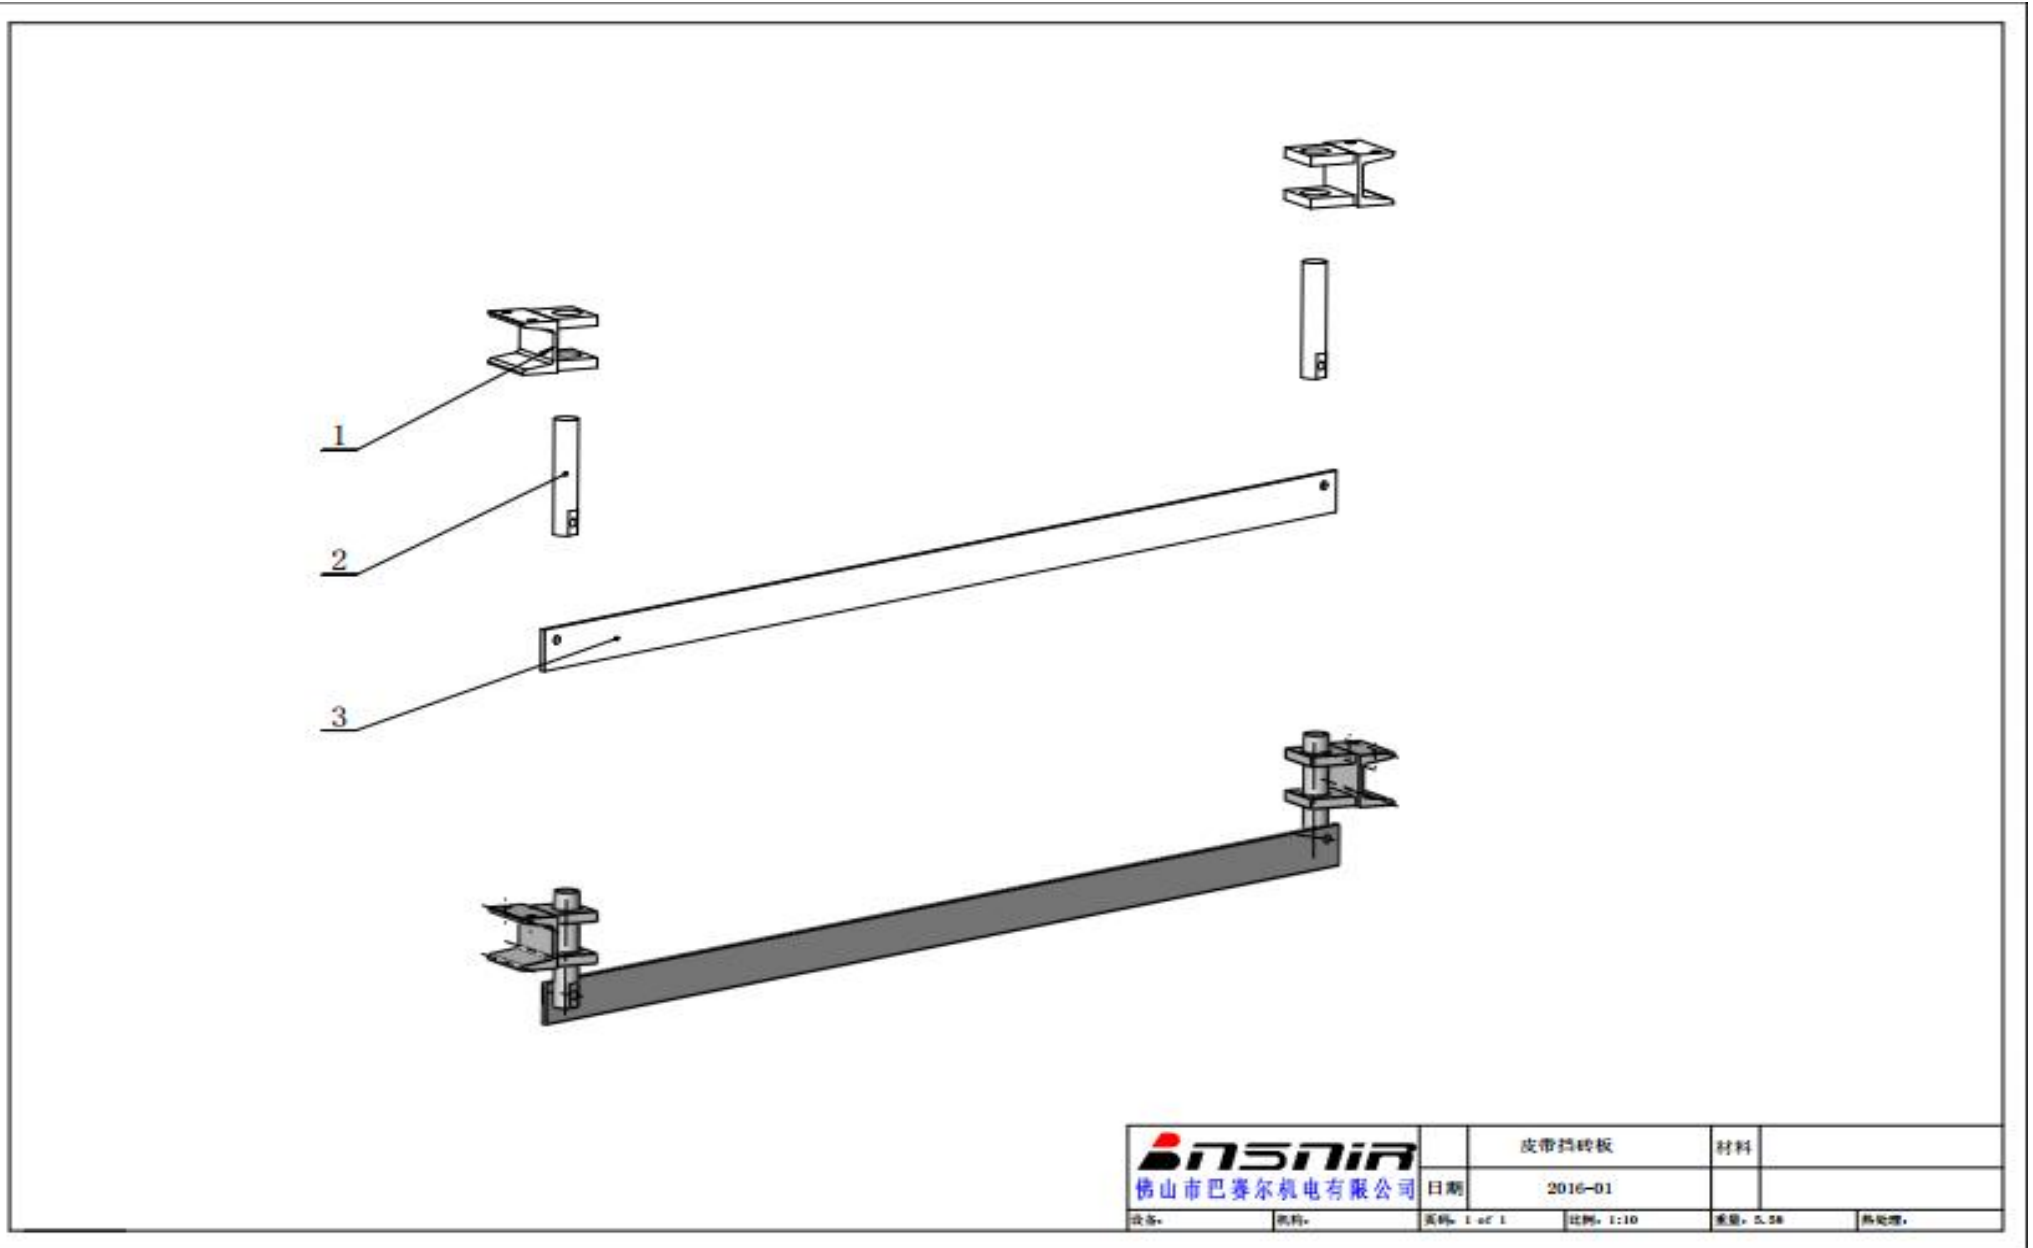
6 机架部分——皮带挡砖板装配图 picture 2-6 Rack part -- belt block board assembly drawing
